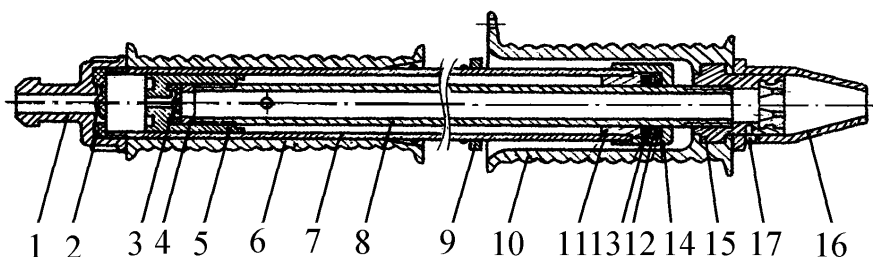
Гидропульт: 1 – штуцер; 2 – основной клапан; 3 – клапан цилиндра; 4 – втулка штока; 5 – поршень; 6 – ручка-держатель; 7 – цилиндр; 8 – шток; 9 – ограничитель; 10 – ручка-распылитель; 11 – втулка цилиндра; 12 – поджимное кольцо; 13 – уплотнитель; 14 – гайка уплотнителя; 15 – наконечник; 16 – колпачок; 17 – винтовой фиксатор
